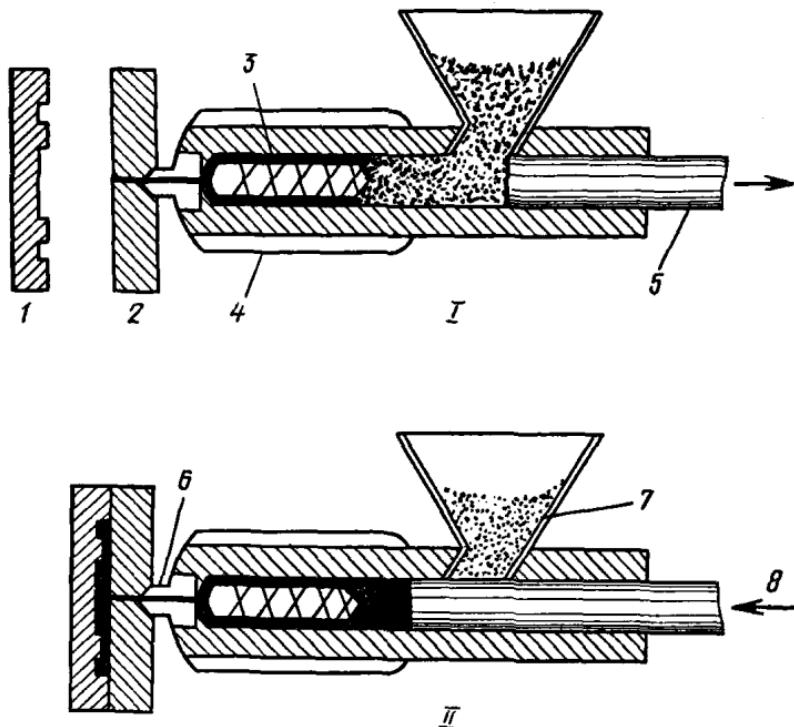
Схема изготовления изделий из пластмасс литьем под давлением:
